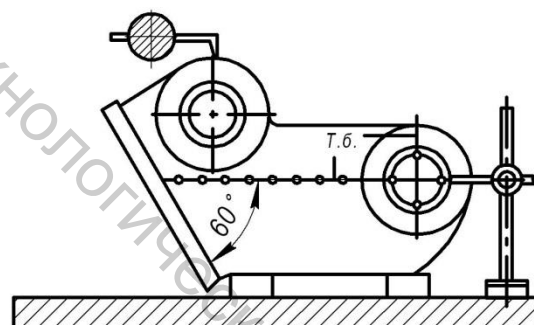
Реальное базирование заготовки на столе станка
